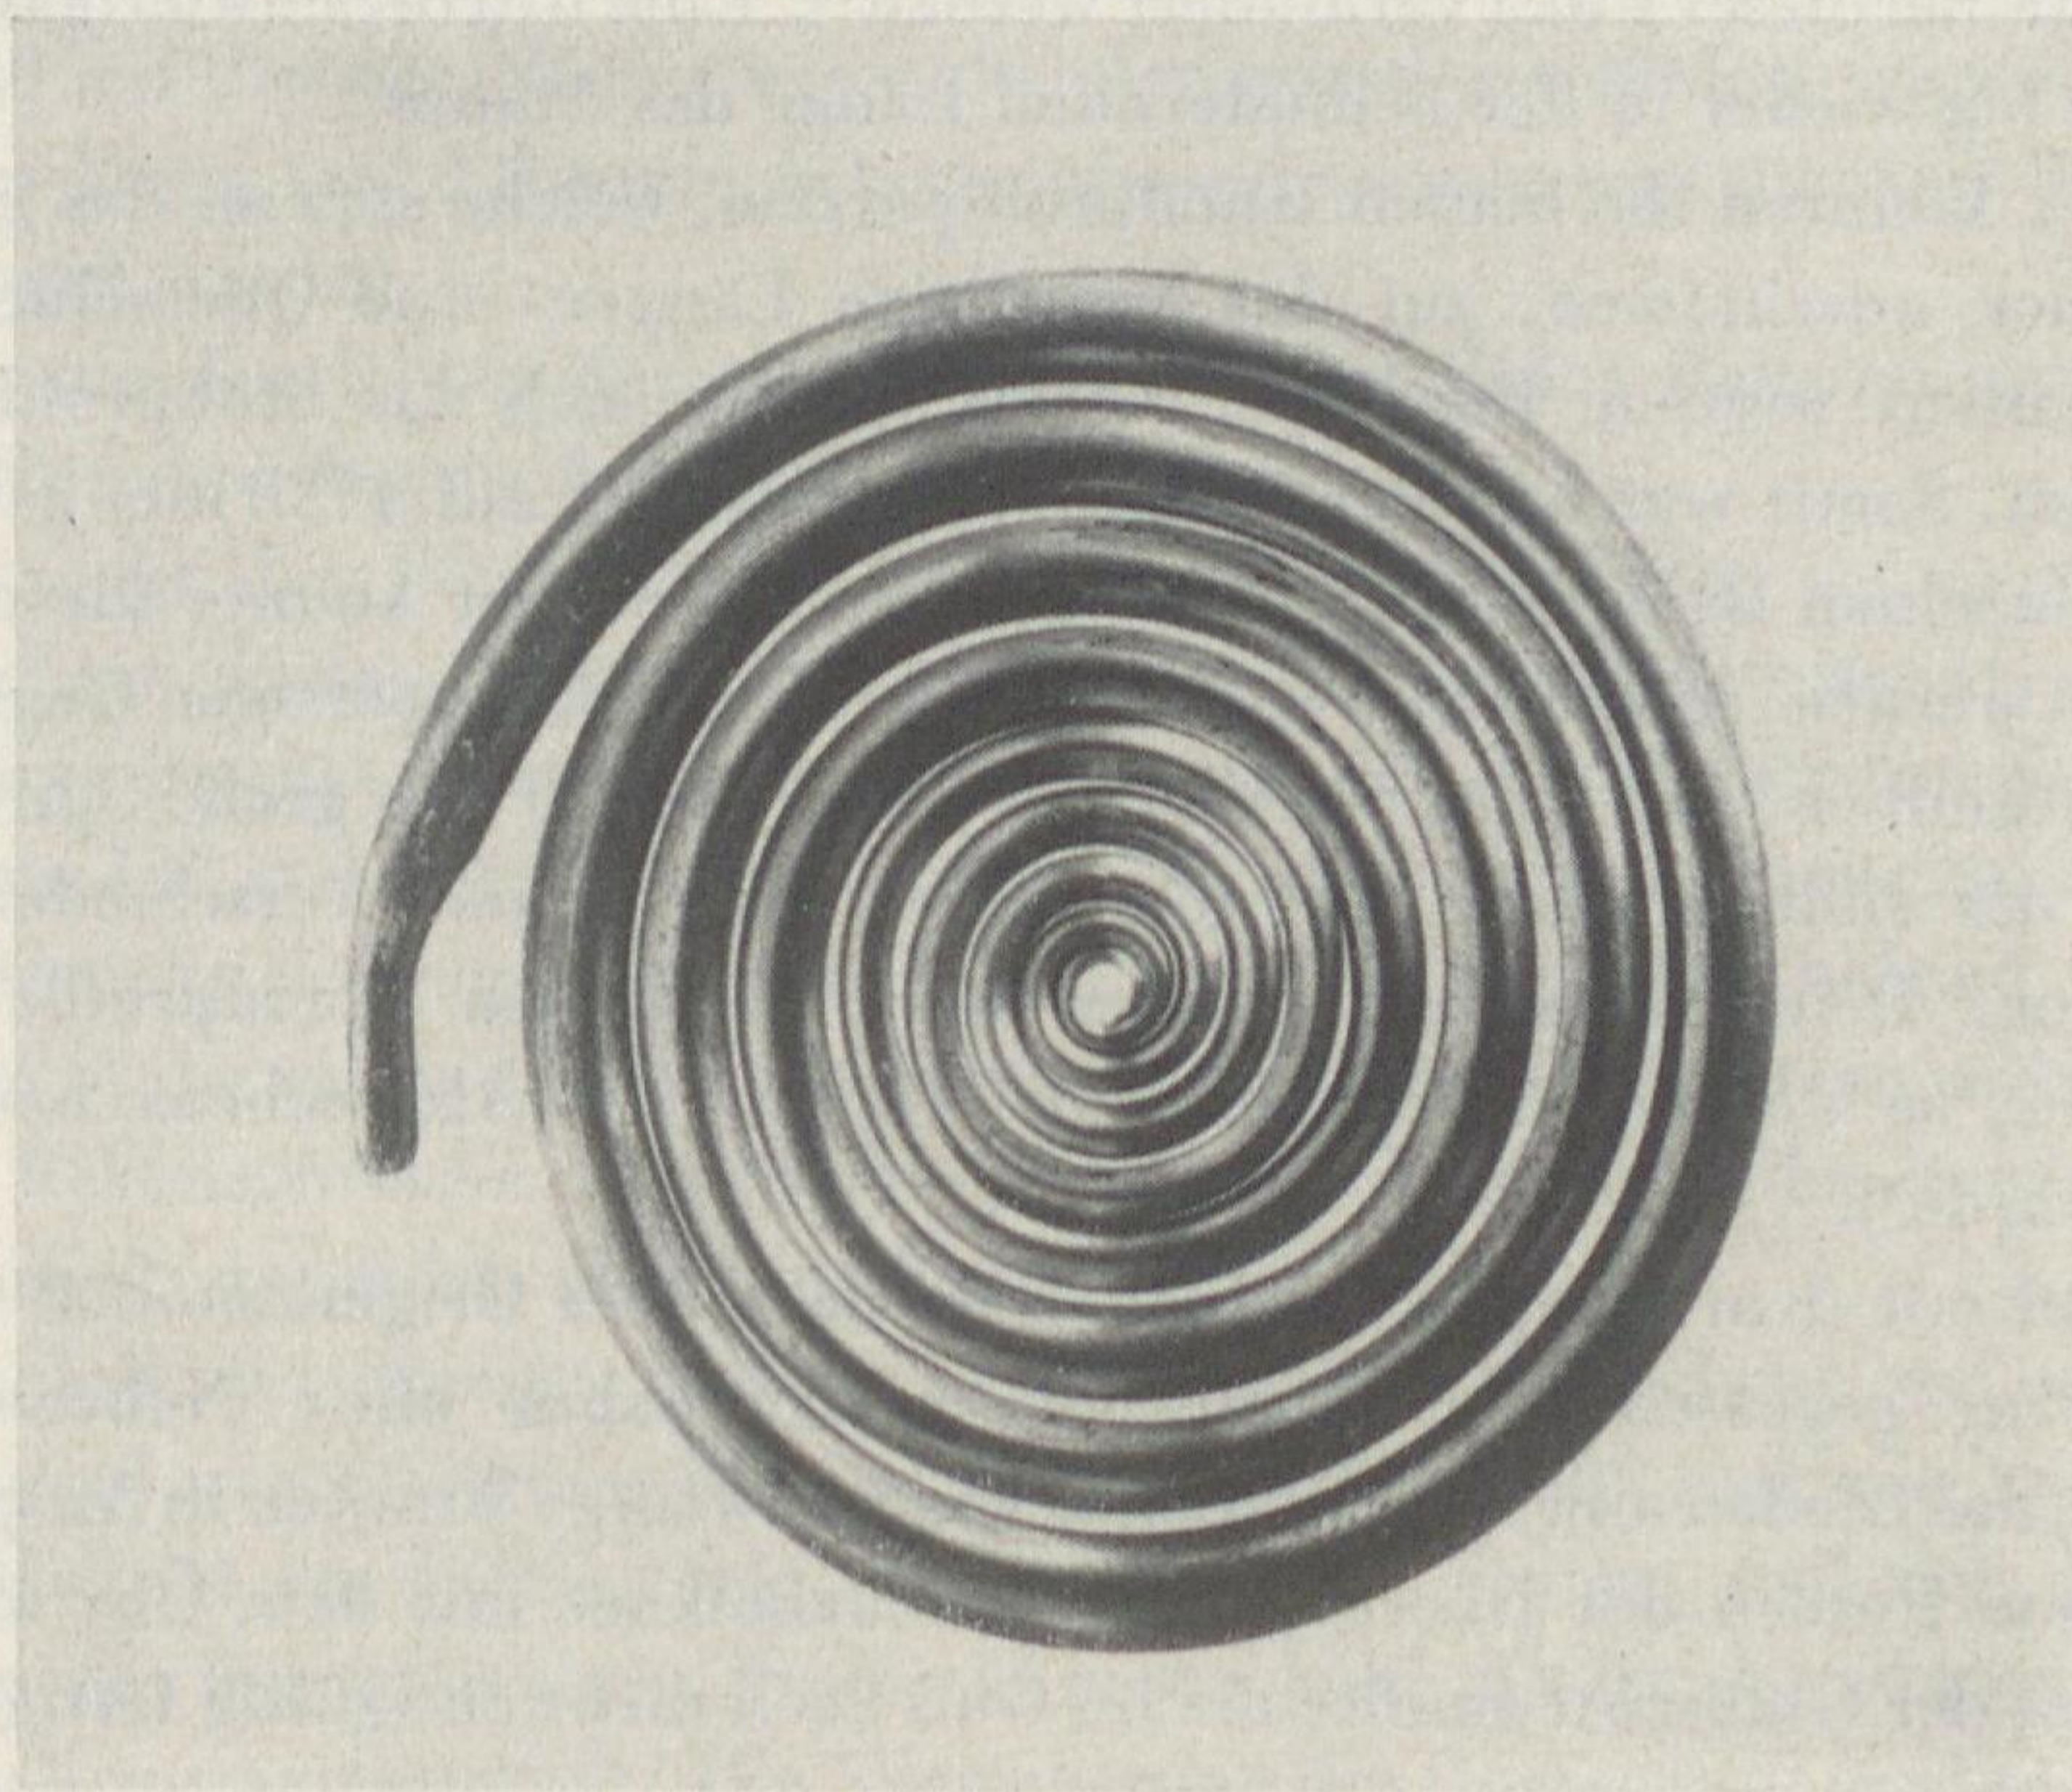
Drehprobe für die Spiralplatten. 1:1.
